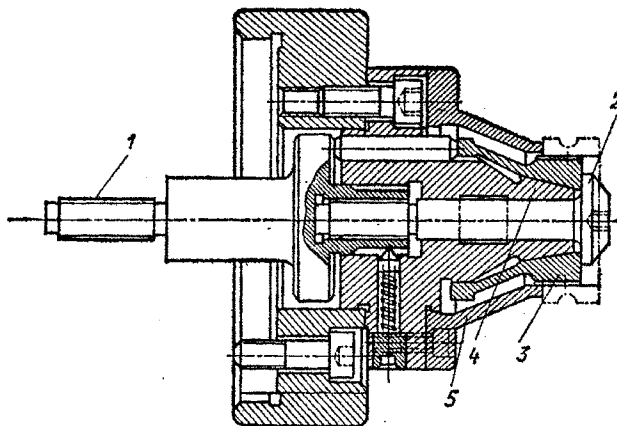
Цанговий механізм для затискання заготовки по внутрішньому діаметру
